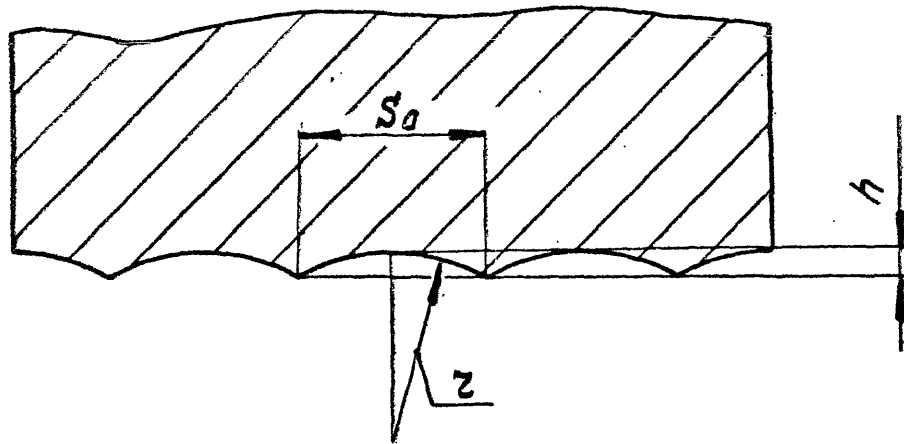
Профиль поверхности, обработанной резцом с радиусной режущей кромкой.
